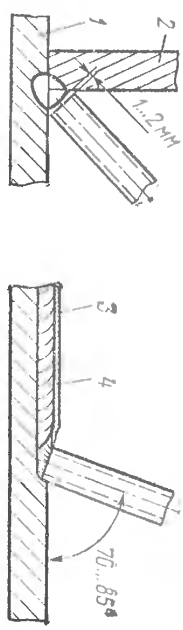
Схема сварки ультракороткой дугой с глубоким проплавлением: 1, 2 — свариваемые заготовки, 3 — шлак, 4 — наплавленный металл
